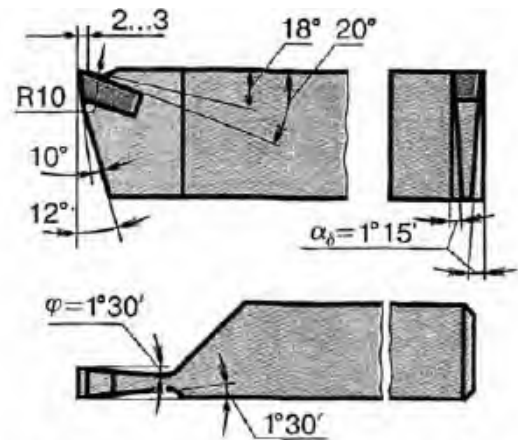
ПРОРІЗНИЙ ТВЕРДОСПЛАВНИЙ РІЗЕЦЬ
